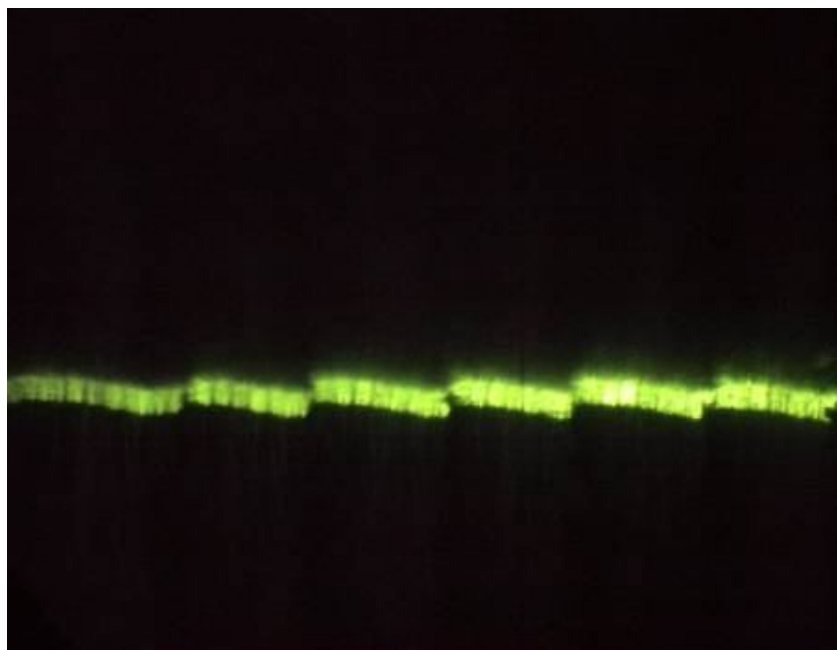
Шероховатость поверхности стали с применением СОЖ - Аквол-11 при черновой обработке.
